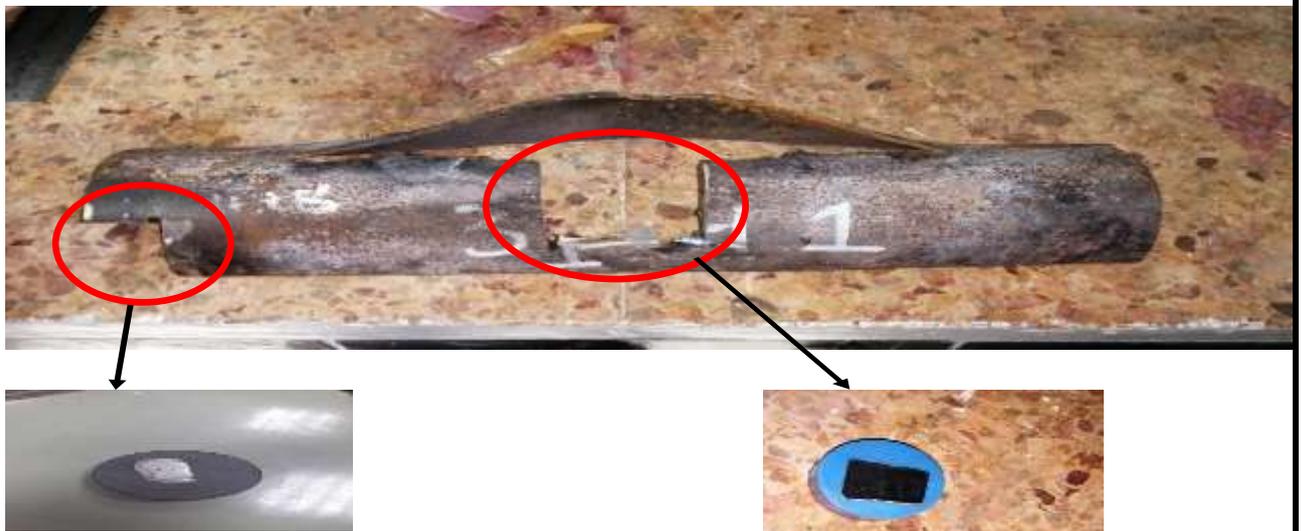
Découpage de la pièce et enrobage des échantillons
